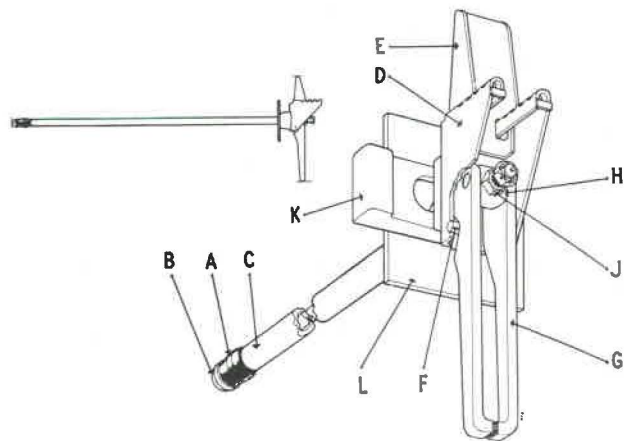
Boulon récupérable Dowty utilisé pour le calage des bossements.
